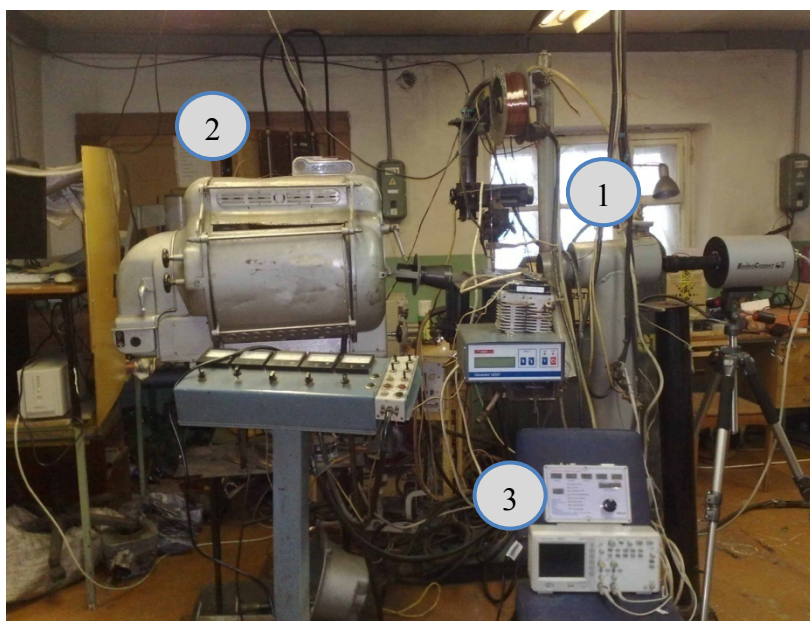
Экспериментальный комплекс: 1 – сварочная головка ГСП-2 укомплектованная механизмом импульсной подачи электродной проволоки; 2 – смесительное оборудование; 3 – цифровой регистратор параметров сварки
